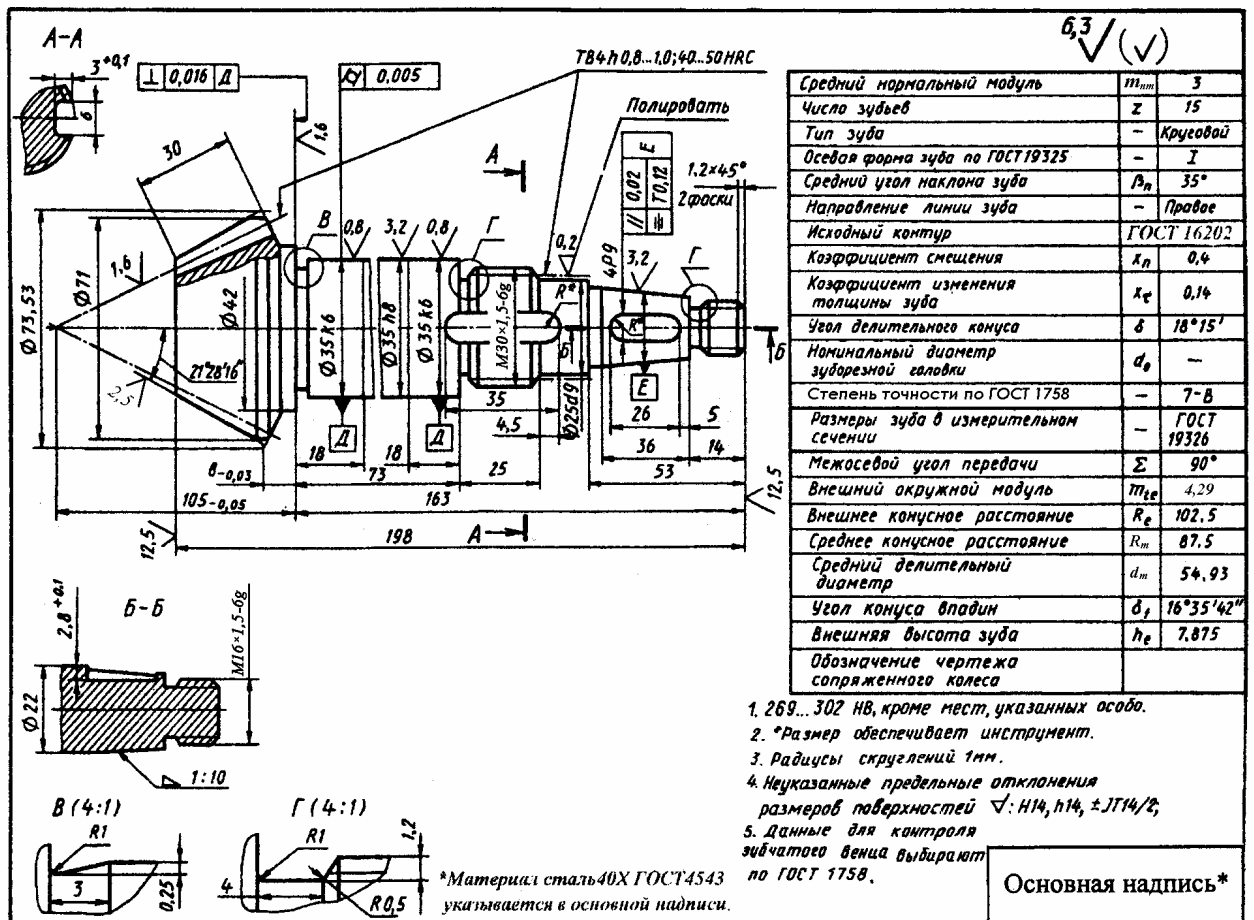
Рабочий чертеж вала - шестерни (конической)
